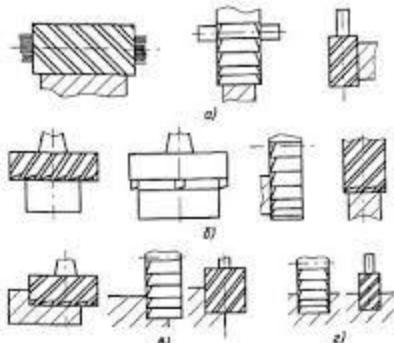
Схемы фрезерования плоских поверхностей:
